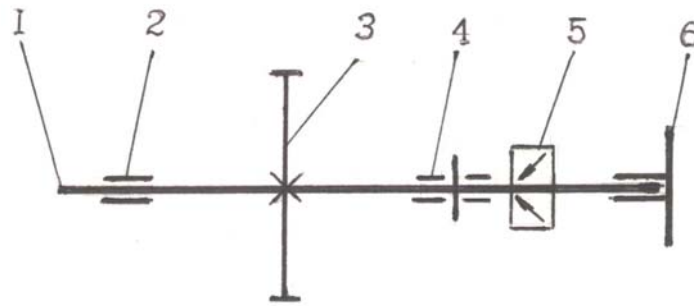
Схема розташування деталей на вхідному валу редуктора:
